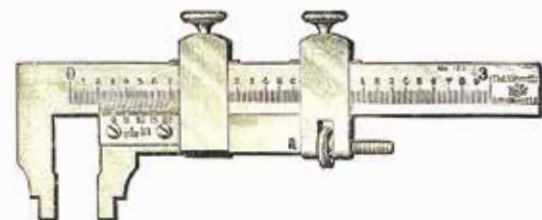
Calibrador vernier de bolsillo de L.S. Starrett Co.
